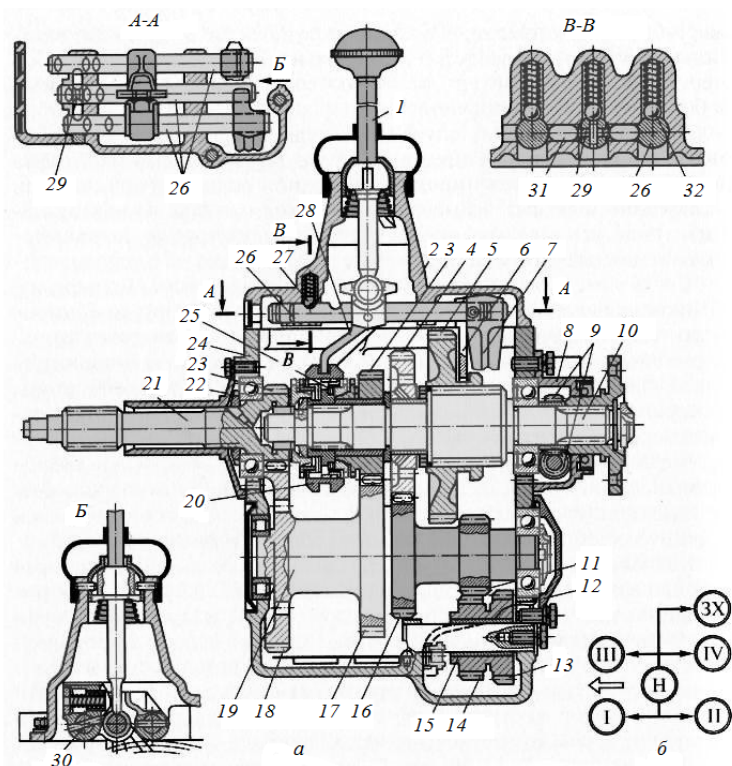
Коробка передач автомобиля ГАЗ-3307: *а* – устройство: 1 – рычаг; 2, 8, 12, 22 – крышка; 3 – шестерня; 4, 5, 13, 17, 18 – зубчатые колеса; 6, 7, 28 – вилки переключения передач; 9 – червячная пара привода спидометра; 10 – ведомый вал; 11, 14, 16, 23 – прямозубая шестерня; 15 – блок зубчатых колес заднего хода; 19 – промежуточный вал; 20 – муфта синхронизатора; 21 – ведущий вал; 24 – картер; 25 – синхронизатор; 26 – ползун; 27 – фиксатор; 29 – штифт; 30 – предохранитель; 31 – плунжер; 32 – шарик с пружинами; *б* – схема переключения передач: I, II, III, IV и 3X – положение рычага 1, соответствующее включению первой, второй, третьей, четвертой передачи и передачи заднего хода; H – нейтральное положение рычага
